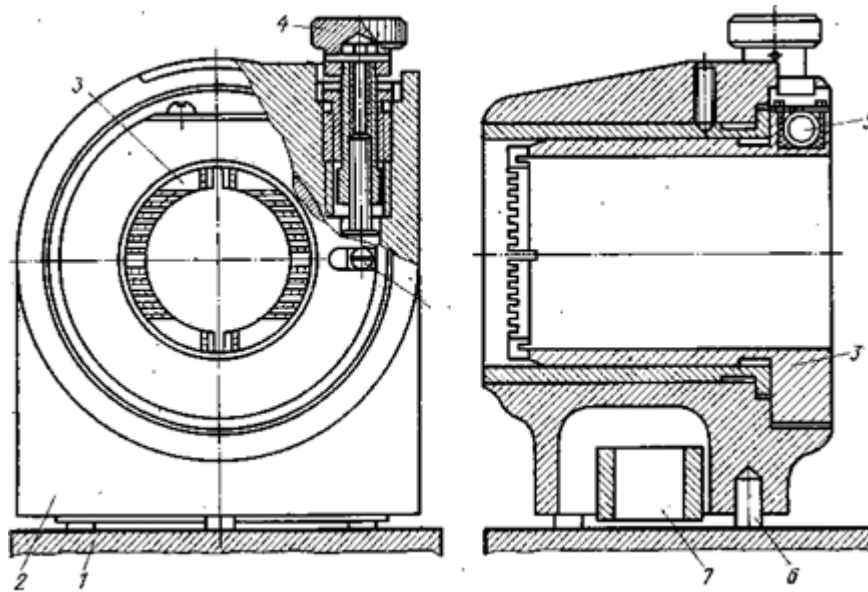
Візир: 1 - горизонтальний роз'єм циліндра (корпусу підшипника), 2 - корпус, 3 - марка, 4 - пристосування для повороту марки, 5 - рівень марки, 6 - опорний штифт, 7 - магнітна основа.
